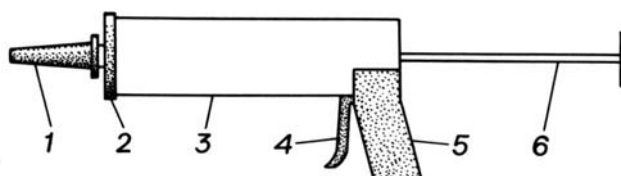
Приспособление для выдавливания клея из картуша: 1 – насадка; 2 – крышка; 3 – корпус; 4 – рычаг; 5 – рукоятка; 6 – шток
